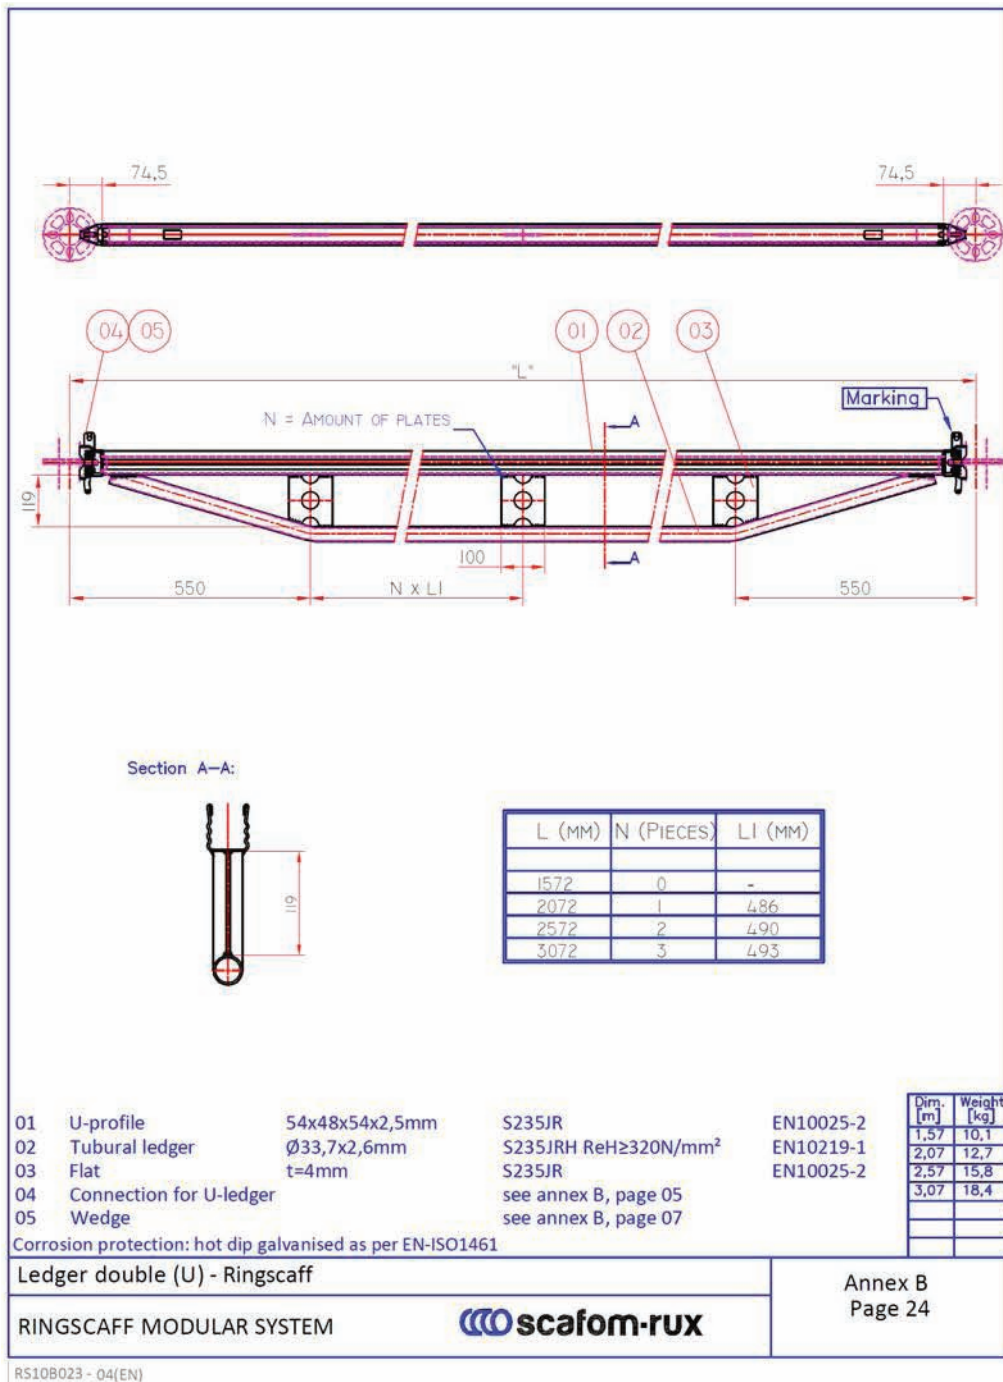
Travessa com dupla secção (em U e tubular)
